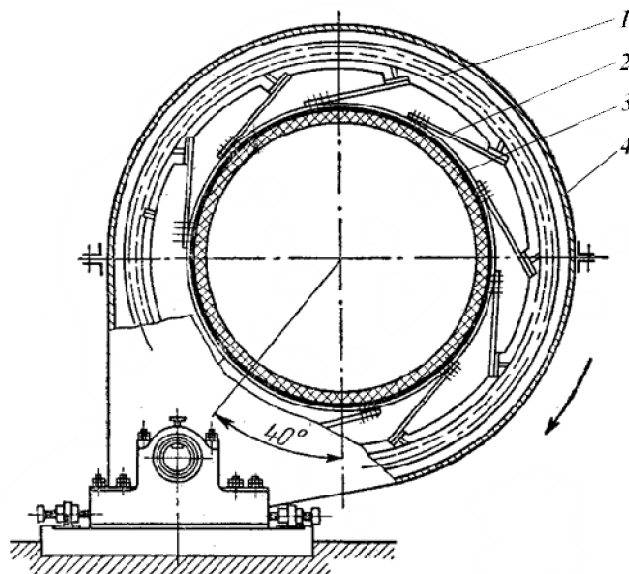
Крепление зубчатого венца к барабану при помощи тангенциально расположенных пружин:
